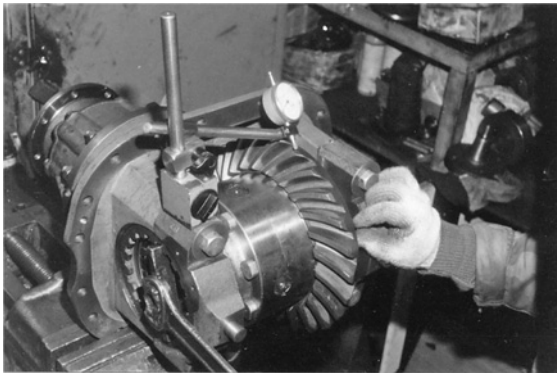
Регулировка параметров зацепления и преднатяга подшипников дифференциала в редукторе ведущего моста автомобиля
